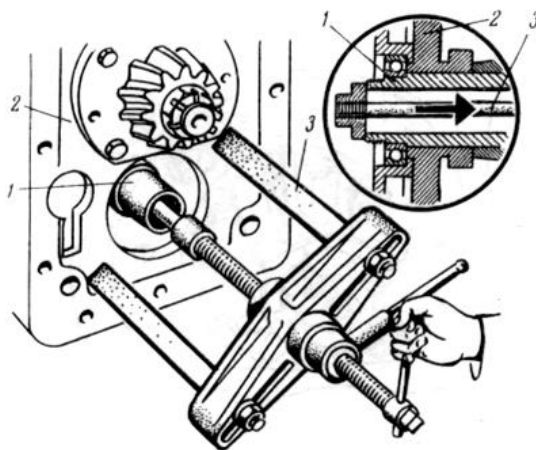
Випресування проміжного вала: 1- проміжний вал; 2- корпус коробки передач; 3- знімач
